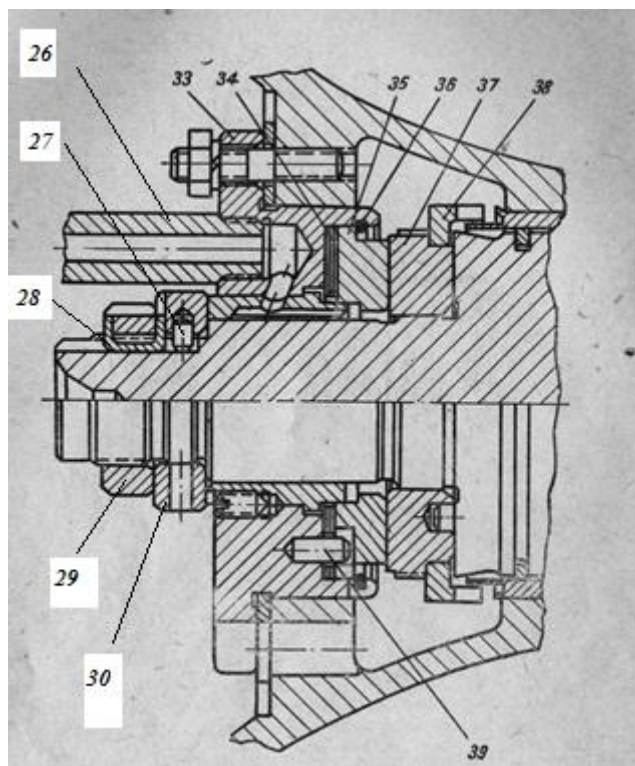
Упорно-опорний підшипник: 26 – штуцер підведення масла; 27 – штифт; 28 – замкова пластина; 29 – гайка; 30 – допоміжна упорна п'ята, 33 – корпус підшипника; 34 – набір платівок; 35 – підп'ятник; 36 – стопорне кільце; 37 – п'ята; 38 – імпелер; 39 – штифт
